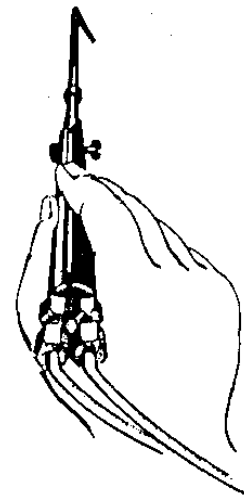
Posição do maçarico para soldar metais de pouca espessura com acetileno.
